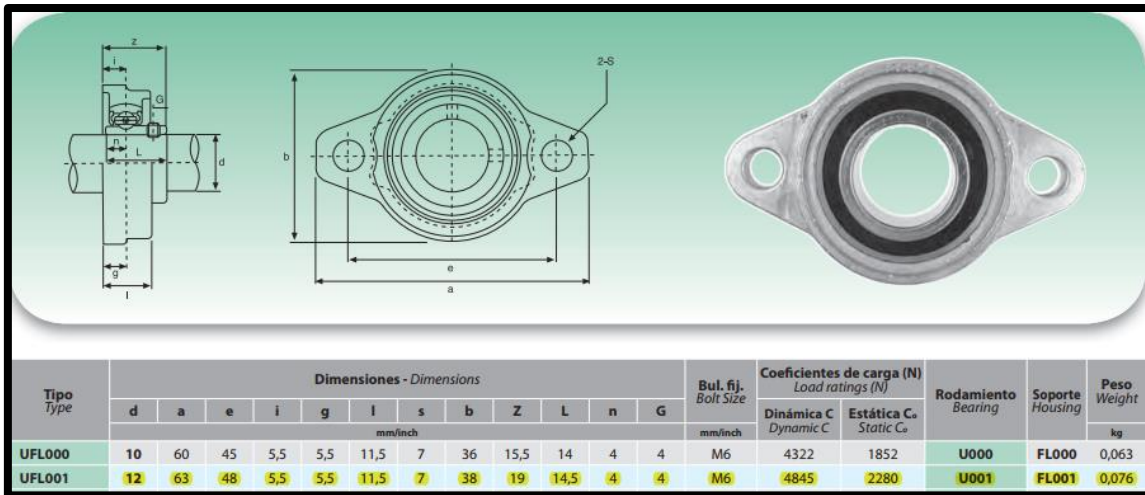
Rodamiento con soporte de 12 mm. Fuente: Catálogo de Rodamientos con Soporte ISB.
